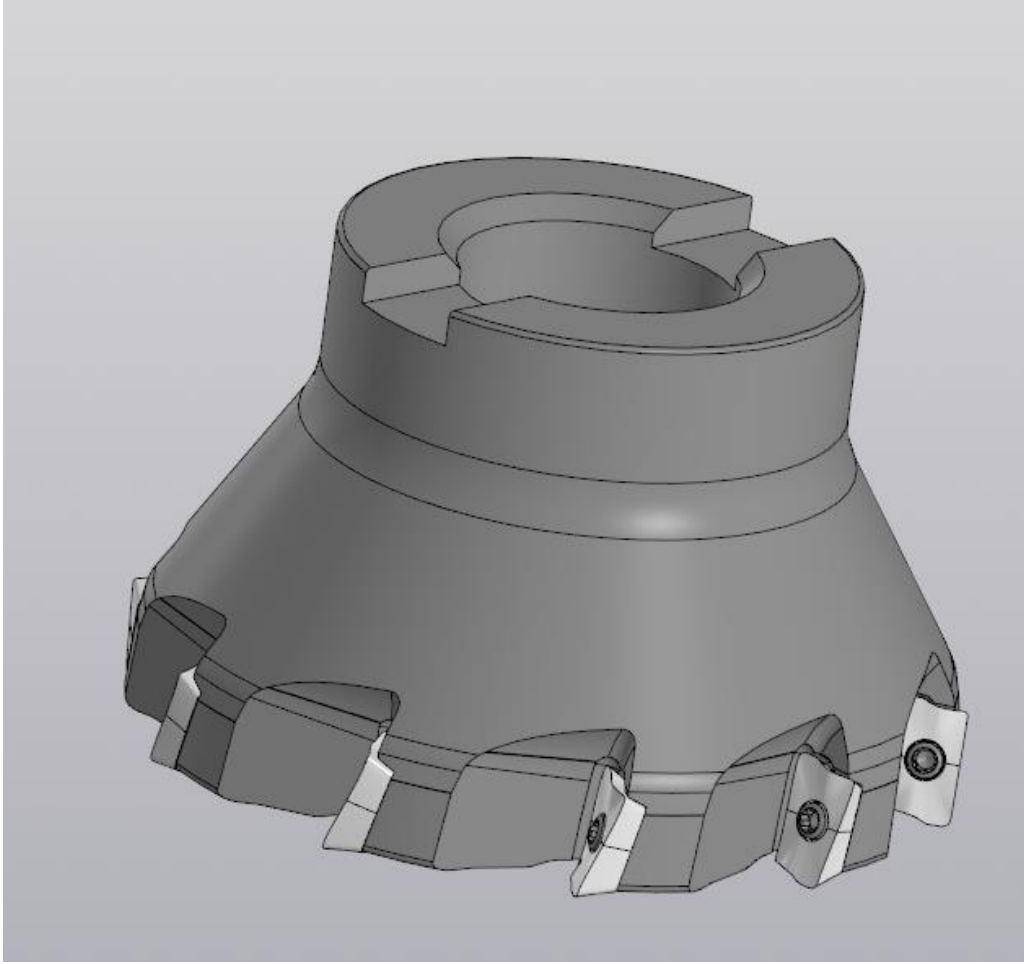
3D вигляд розробленої торцевої фрези
